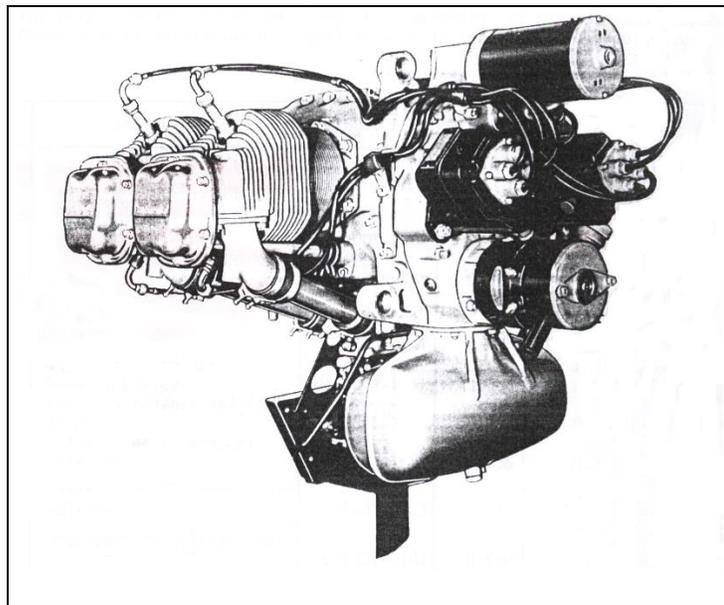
VISTA LATERAL IZQUIERDA MOTOR "O-200A"
